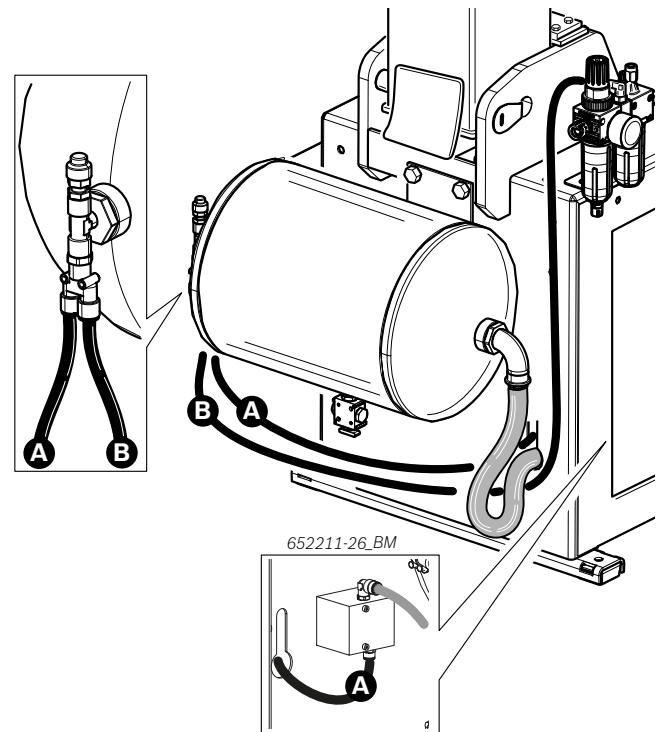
Druckluftanschlüsse für Druckluftbehälter
